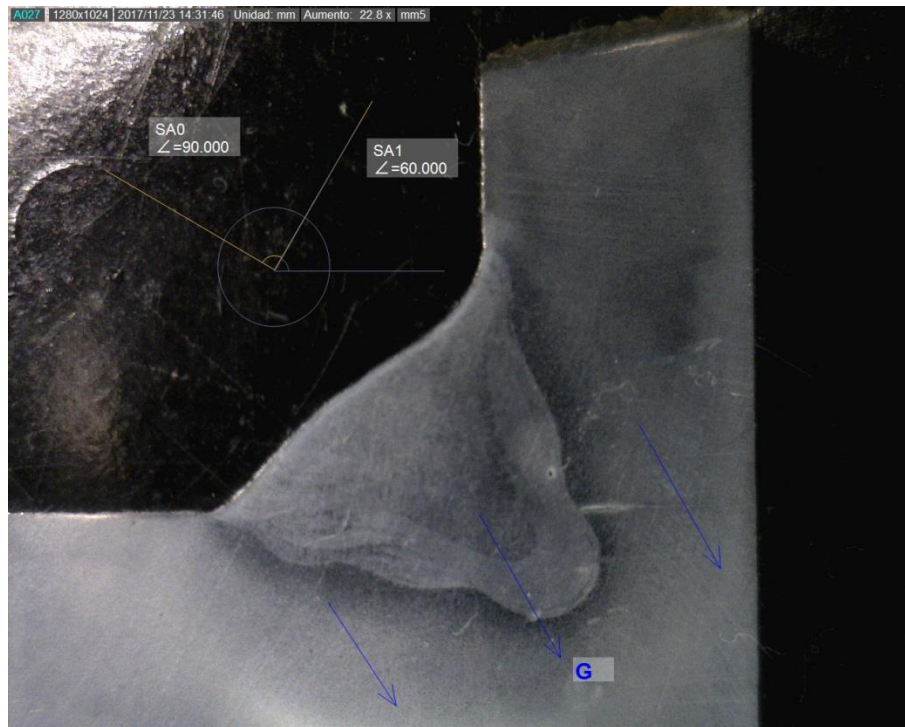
3 Perfil obtenido en cupón de soldadura 2A.
